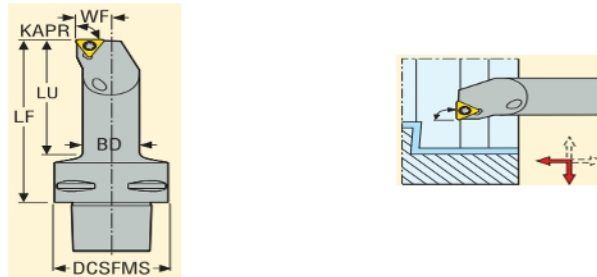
Державка C4-STFCR/L-11070-11 [1, с. 343]
